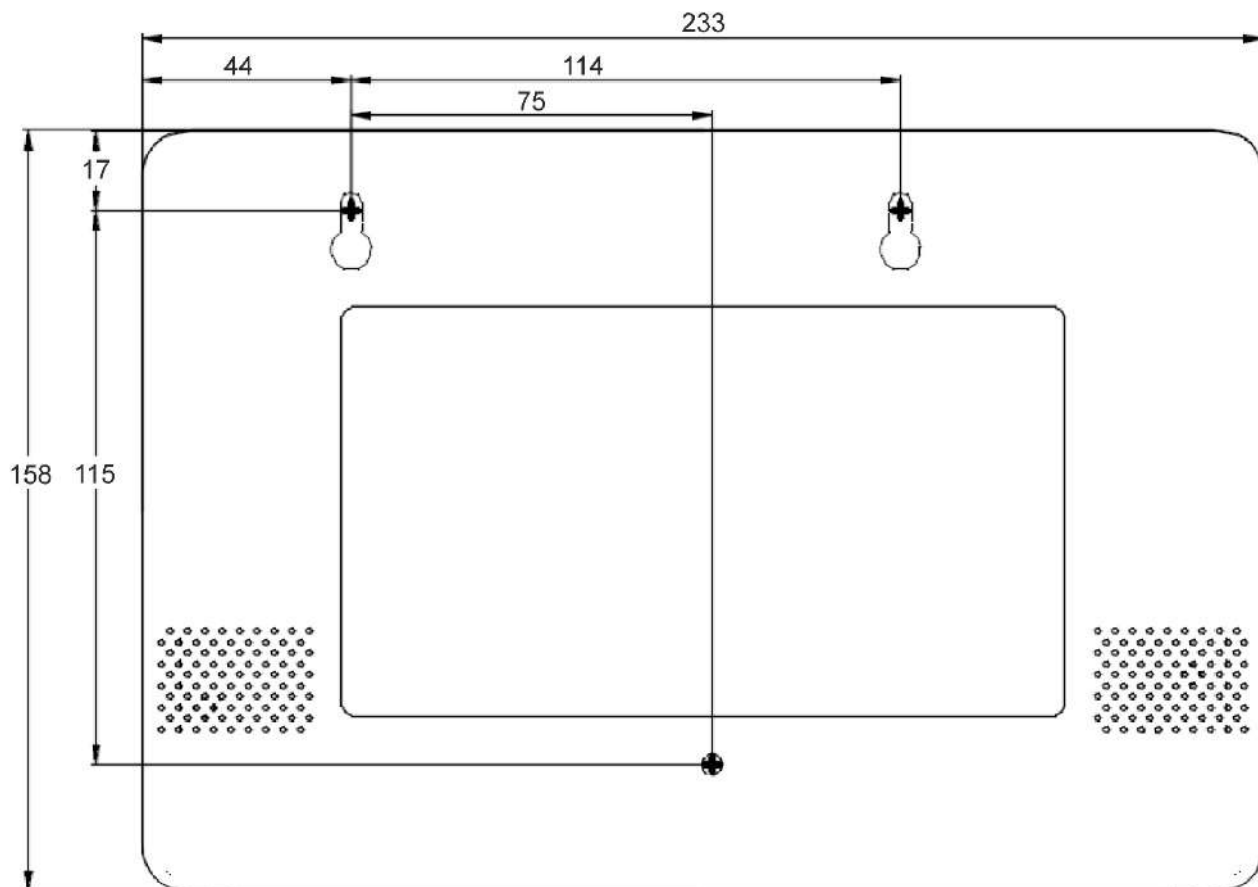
Разметка отверстий для крепления прибора КОП-05
